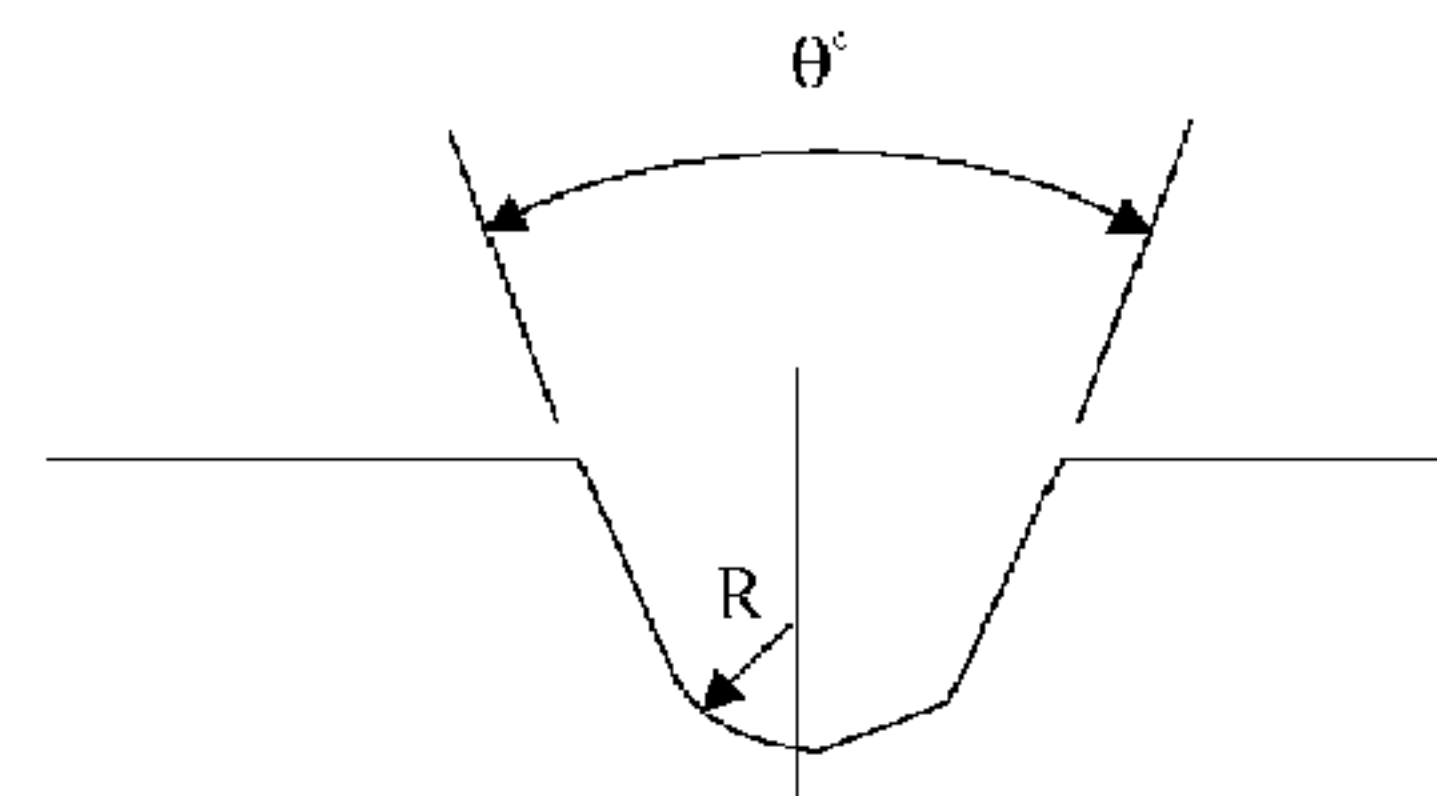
Подготовка под сварку (слева разделка U-образной формы, справа — V-образной формы)
